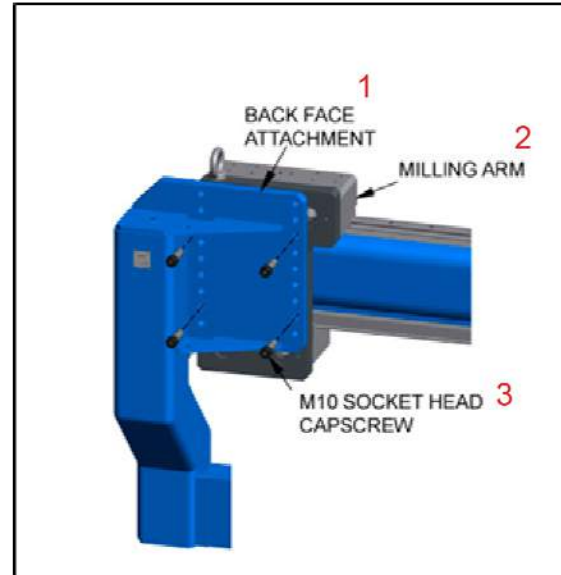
Détail de l'assemblage de la fixation de la face arrière
